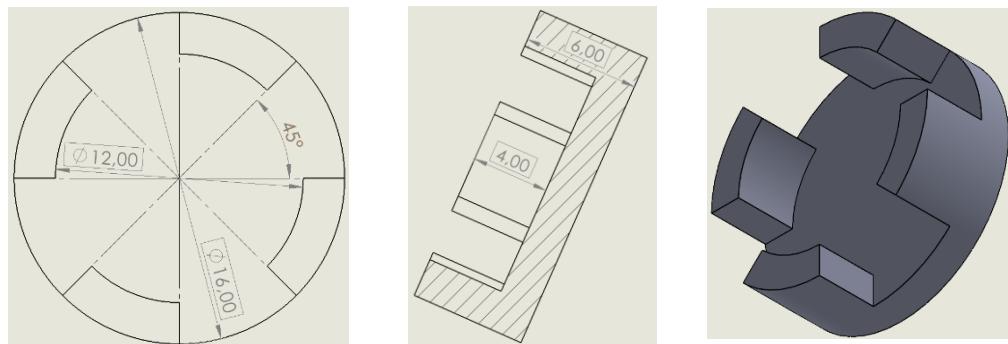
Geometría y dimensiones de la pieza 2, hecha en SolidWorks.
